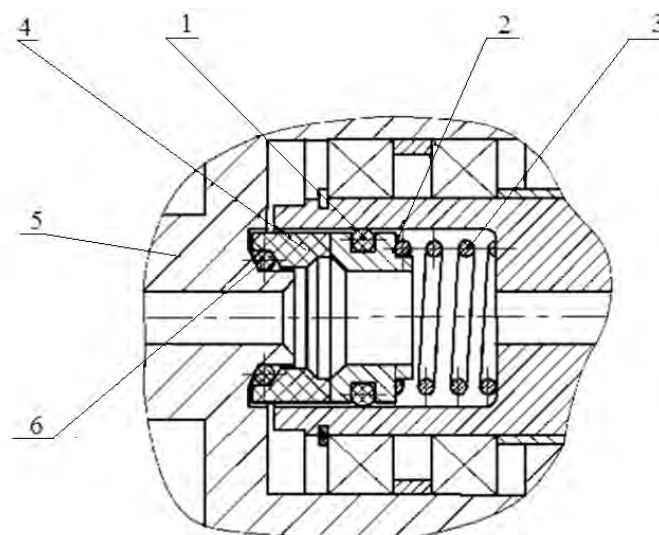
Конструктивна схема розробленого торцевого ущільнення до зовнішньої конусної поверхні циліндричного виступу опорне кільце 7.
